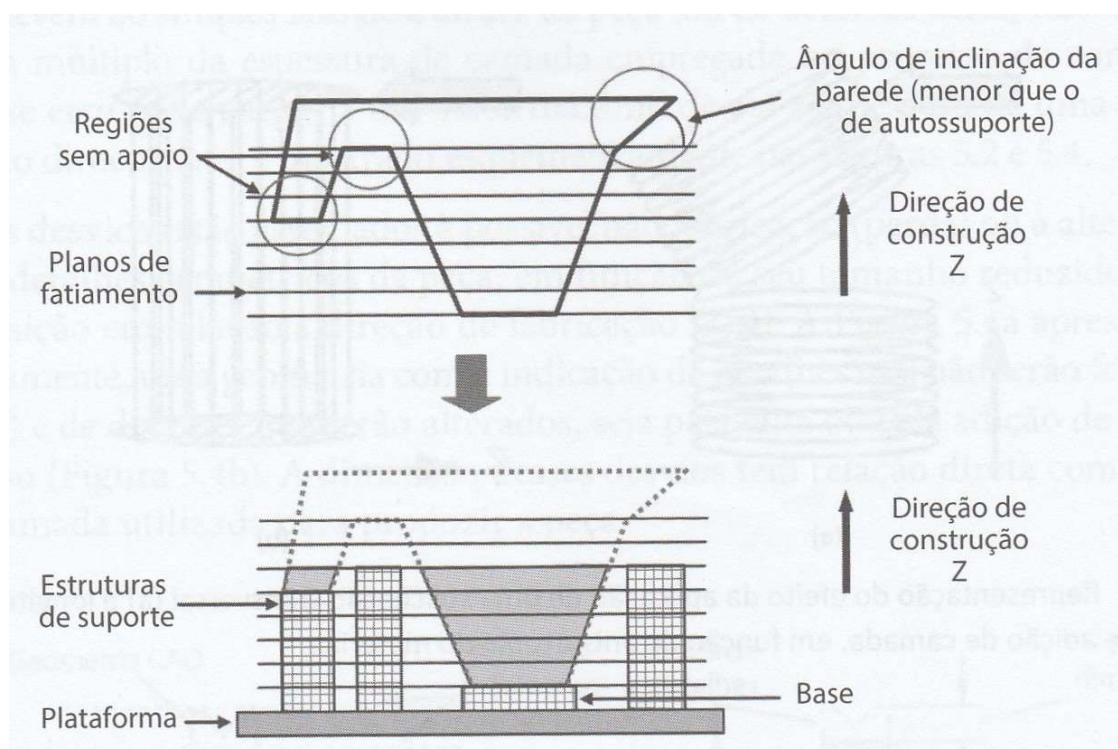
Representação de regiões que requerem estruturas de suporte e da peça sendo construída sobre a base e com as estruturas de suporte em construção [6].
